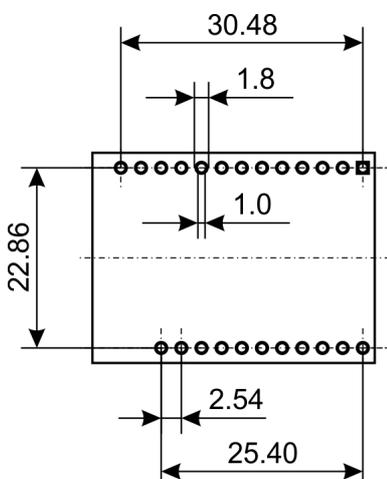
Footprint THT [mm] – Vista dall'alto
